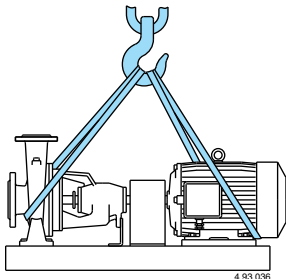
Imbracatura con funi per sollevamento gruppo pompa-motore.
